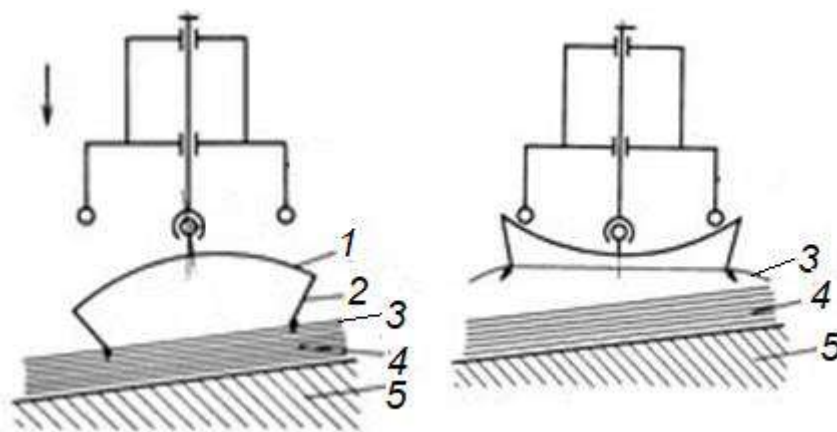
Устройство для захвата верхнего листа из пакета:
